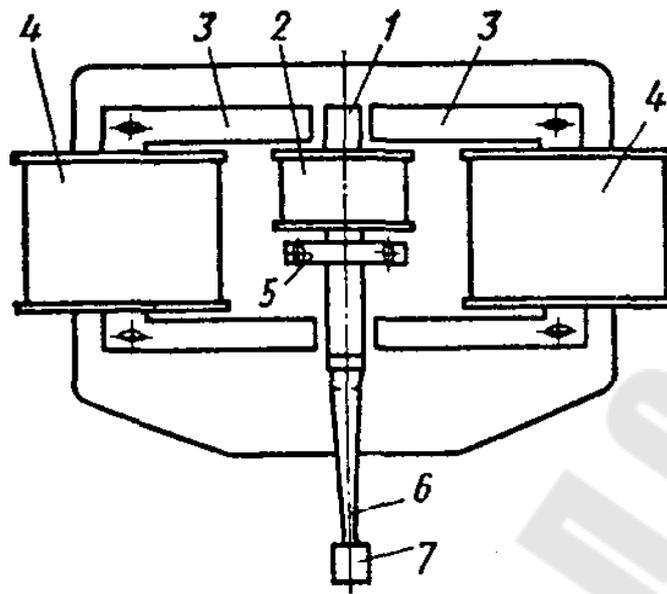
Головка магнестрикционного преобразователя ультразвуковой установки: 1 – сердечник вибратора; 2 – катушка возбуждения; 3 – сердечники; 4 – катушки подмагничивания; 5 – скобы; 6 – трансформатор скорости; 7 – инструмент
